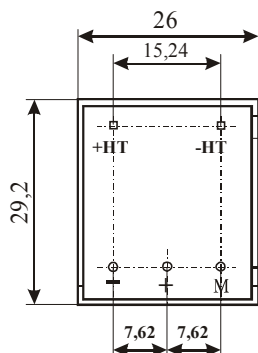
Внешний вид и габаритные размеры датчиков напряжения типа LV 25-P, LV 25-P /SP5
